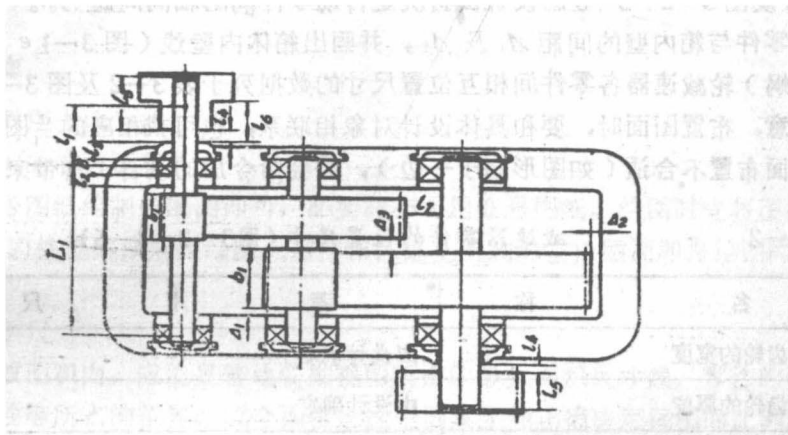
单级圆柱齿轮减速器零件的位置尺寸
